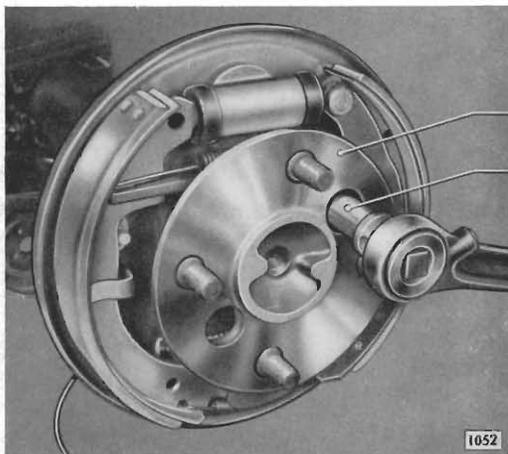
Muttern der Bremshalteschrauben abschrauben
